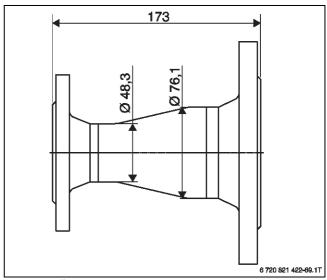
Übergangsstück DN 65/PN 16 – DN 40/PN 6 (Maße in mm)
